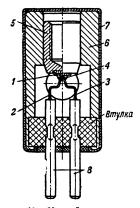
Устройство точенных триодов типов С1 и С2. I — германий; 2 — эмиттер; 3 — коллектор; 4 — заполнитель; 5 — держатель; 6 — корус; 7 — кожух; 8 — вывод.
